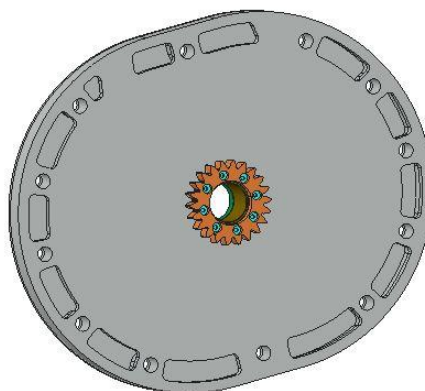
Popis jednotlivých součástí každého ze tří úložných míst
